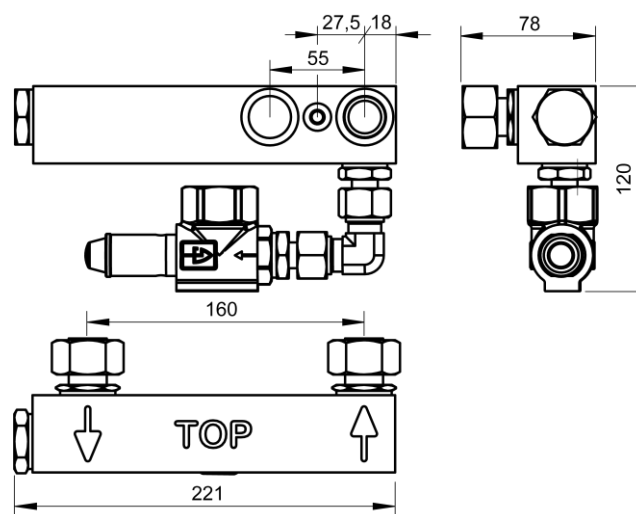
Dimensiones HB-200/230 adaptador para HB-TP180-12
